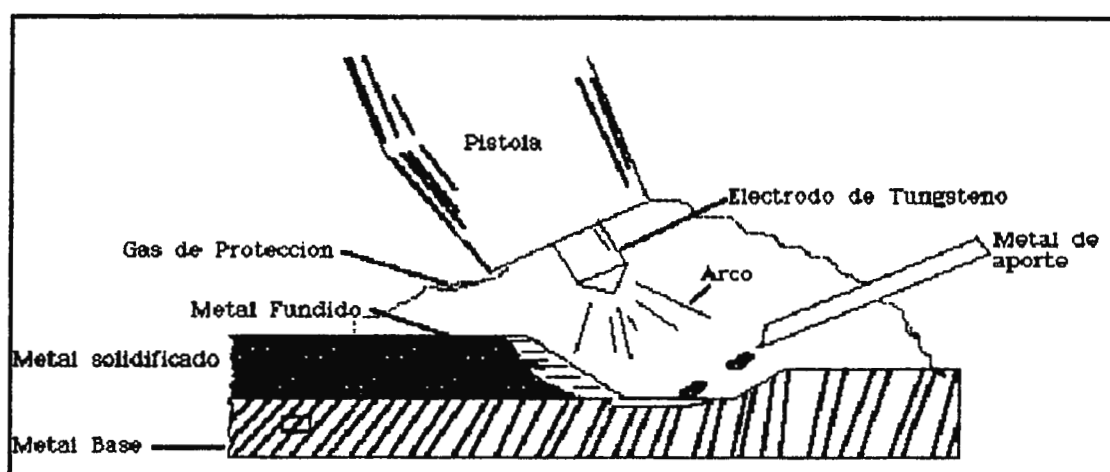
Esquema Soldadura por Sistema TIG
